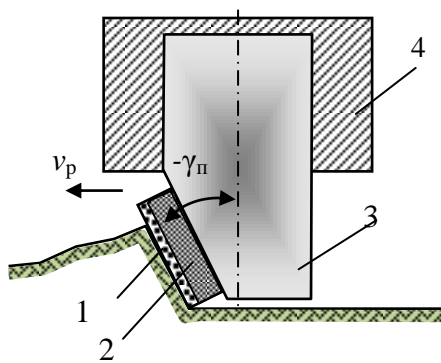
Резец с пластиной PDC: 1 – слой поликристаллических алмазов; 2 – подложка из твердого сплава; 3 – твердосплавная опора; 4 – корпус коронки
